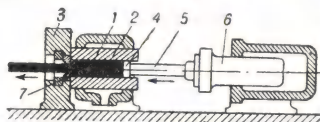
Схема прямого прессования на гидравлическом прессе: 1 — заготовка; 2 — контейнер; 3 — рама; 4 — пресс-шайба; 5 — пуансон; 6 — плунжер; 7 — матрица.
